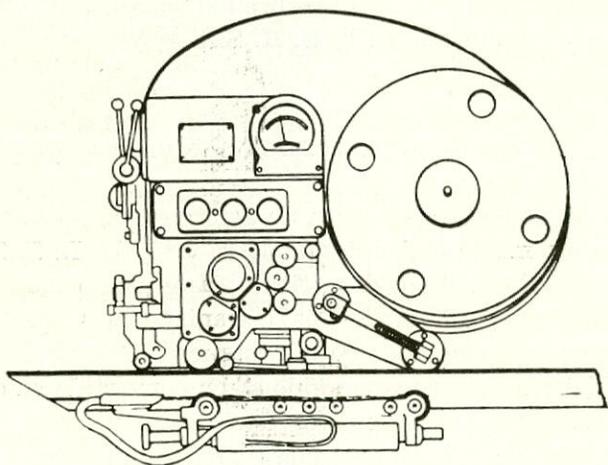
Equipo de soldadura TC-29 con dispositivo especial para la soldadura de costuras a tope de completa penetración.
